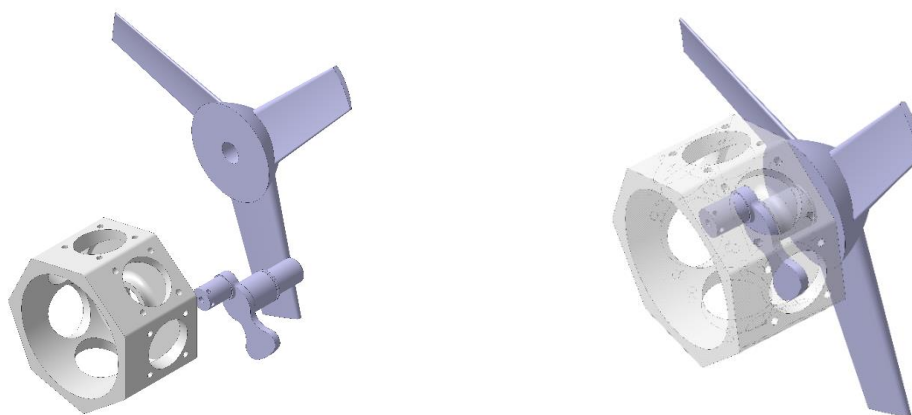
a la izquierda: las tres componentes de la primera unión del conjunto motor. A la derecha: vista del primer ensamble del motor.
